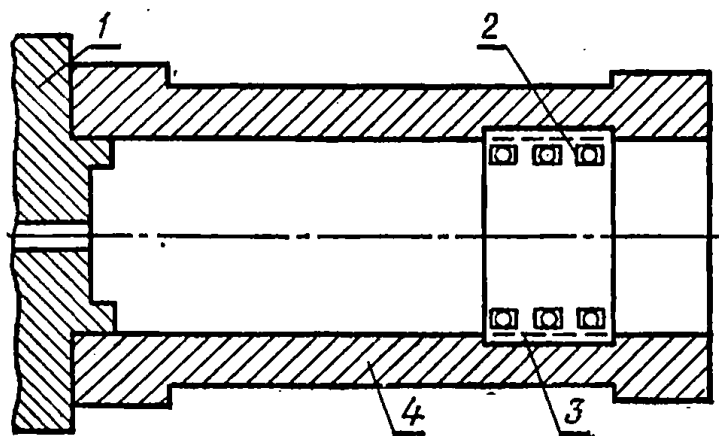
Схема индукционной центробежной наплавки гильз цилиндров:
